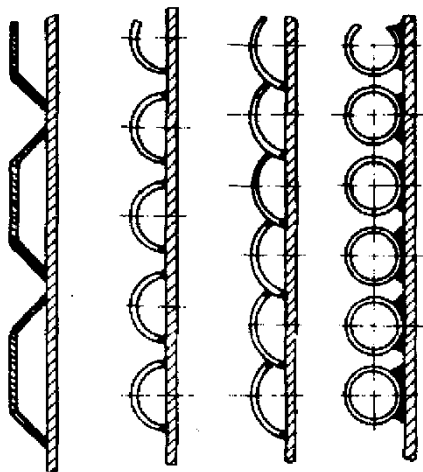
Príklad riešenia ohrevu nádrže parou [4]
